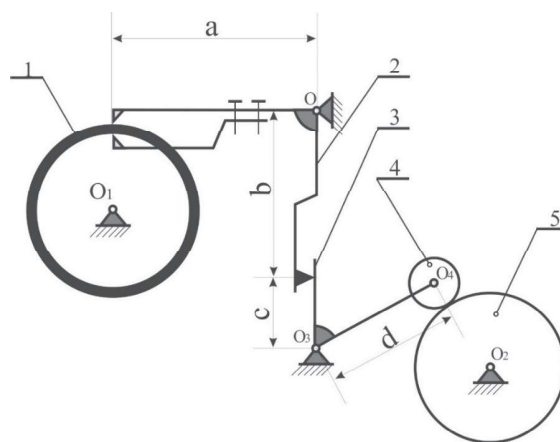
Кинематическая схема копировального узла токарно-копировального полуавтомата МК6026: 1 – пакет заготовок колец; 2 – качающийся суппорт; 3 – двуплечий рычаг; 4 – следящий ролик; 5 – копир
